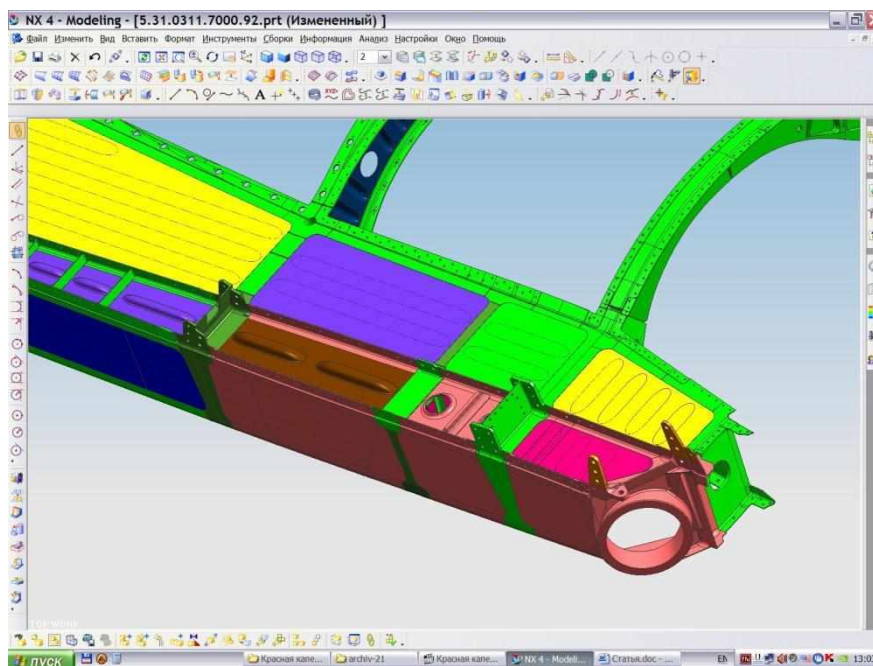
Трехмерная твердотельная сборка конструкции агрегата
